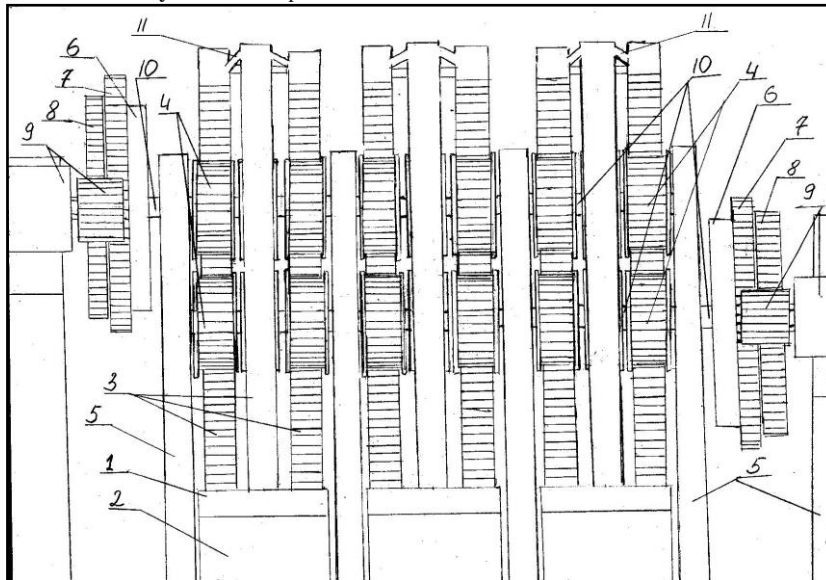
Волновой преобразователь передача с помощью зубчатой рейки, вид с боку.
